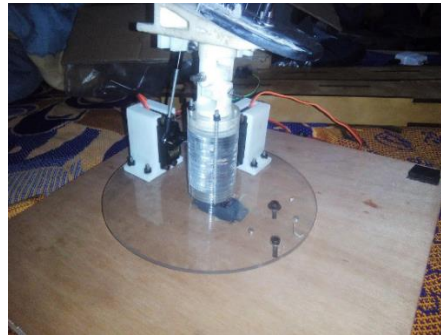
Mecanismo del cuello luego de ser ensamblado con la parte trasera del cráneo.
